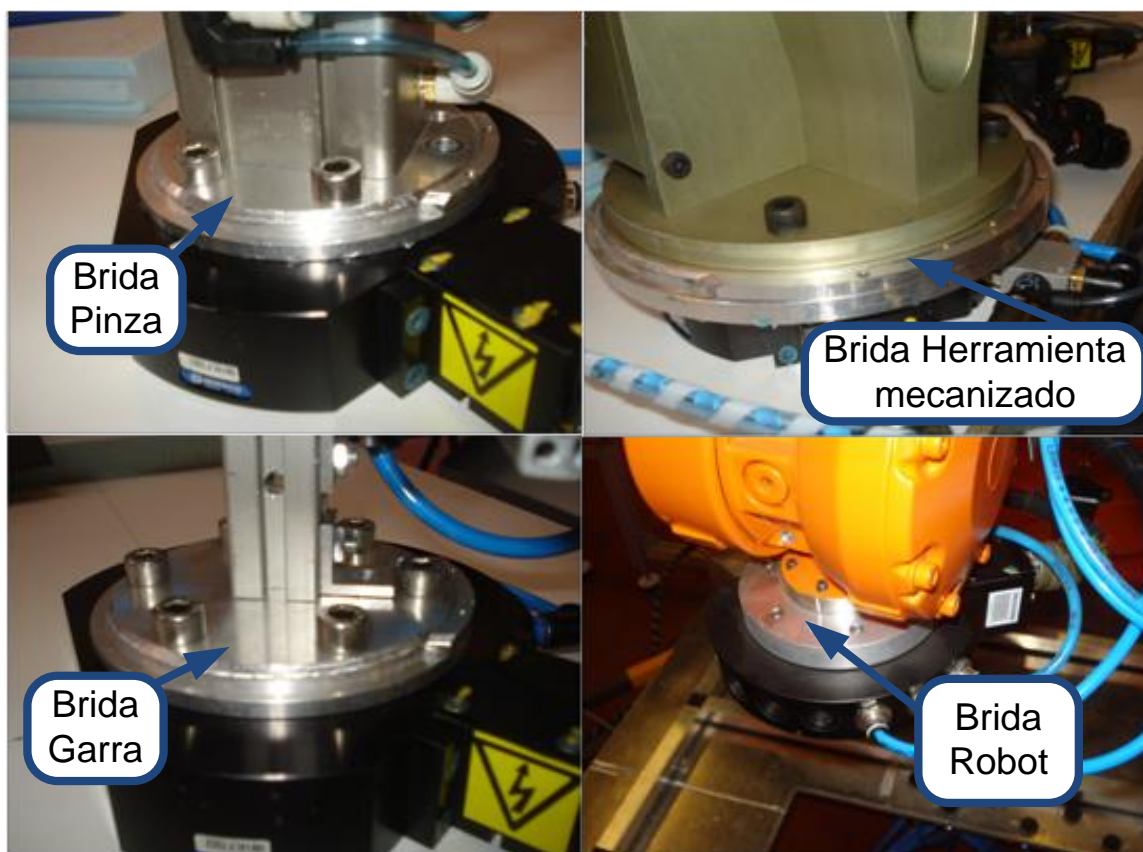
Puesta en marcha de bridas y sus ensamblajes.
